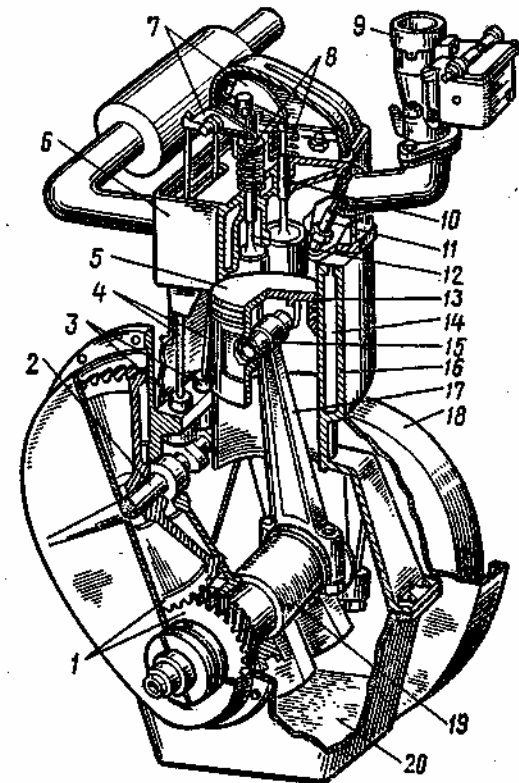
Устройство одноцилиндрового четырёхтактного карбюраторного двигателя
